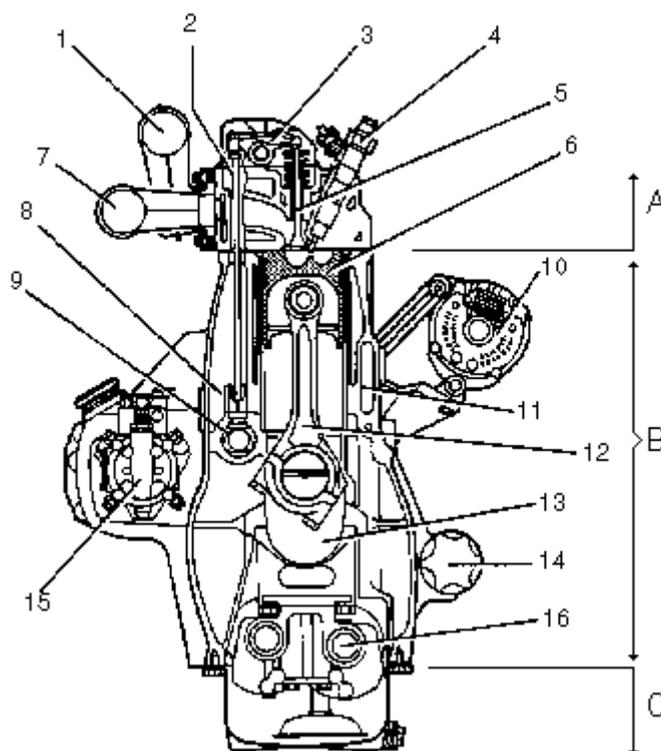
Representação de um corte transversal de um motor Diesel com o veio de excêntricos disposto lateralmente. A- Cabeça motor B- Bloco motor C- Cárter
